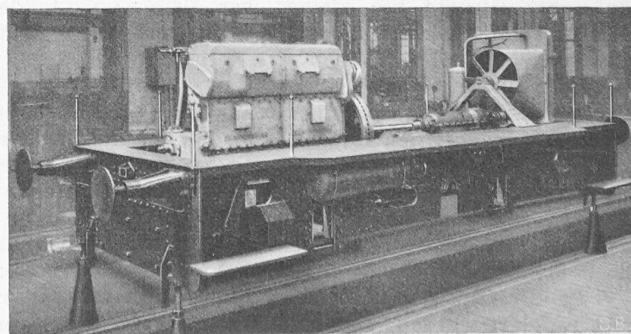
Rahmen der Lokomotive mit aufgebautem Dieselmotor und Kühler.
